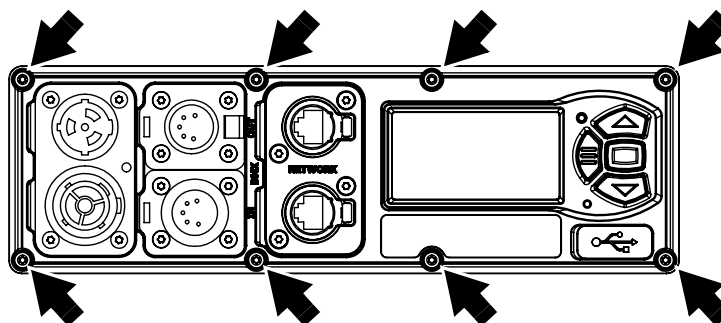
Befestigungsschrauben des Bedienfeldes / Anschlussfeldes
